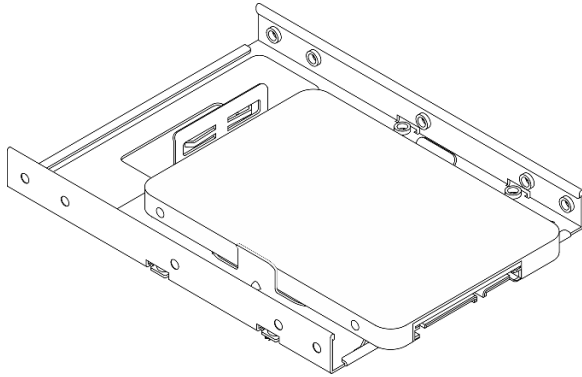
Entfernen des 3,5-Zoll-Laufwerks
